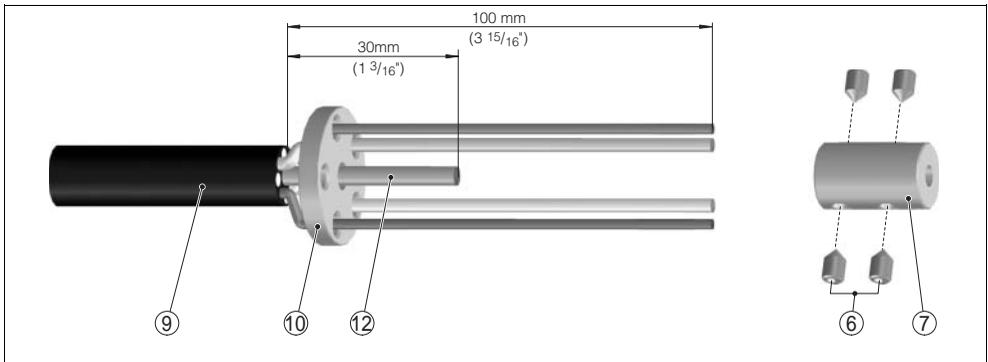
Encurtar o cabo portante - colocar o fixador de cabo
